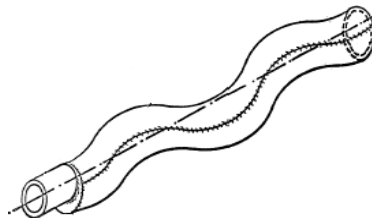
Rotor fabricado por la tecnología combinada de conformado-soldadura (Gunther, 1981).
